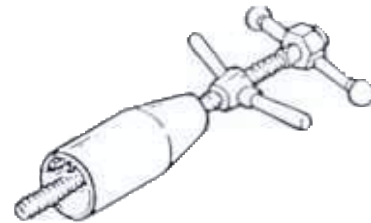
A-14E-03 - Insertador del engranaje del cigüeñal
